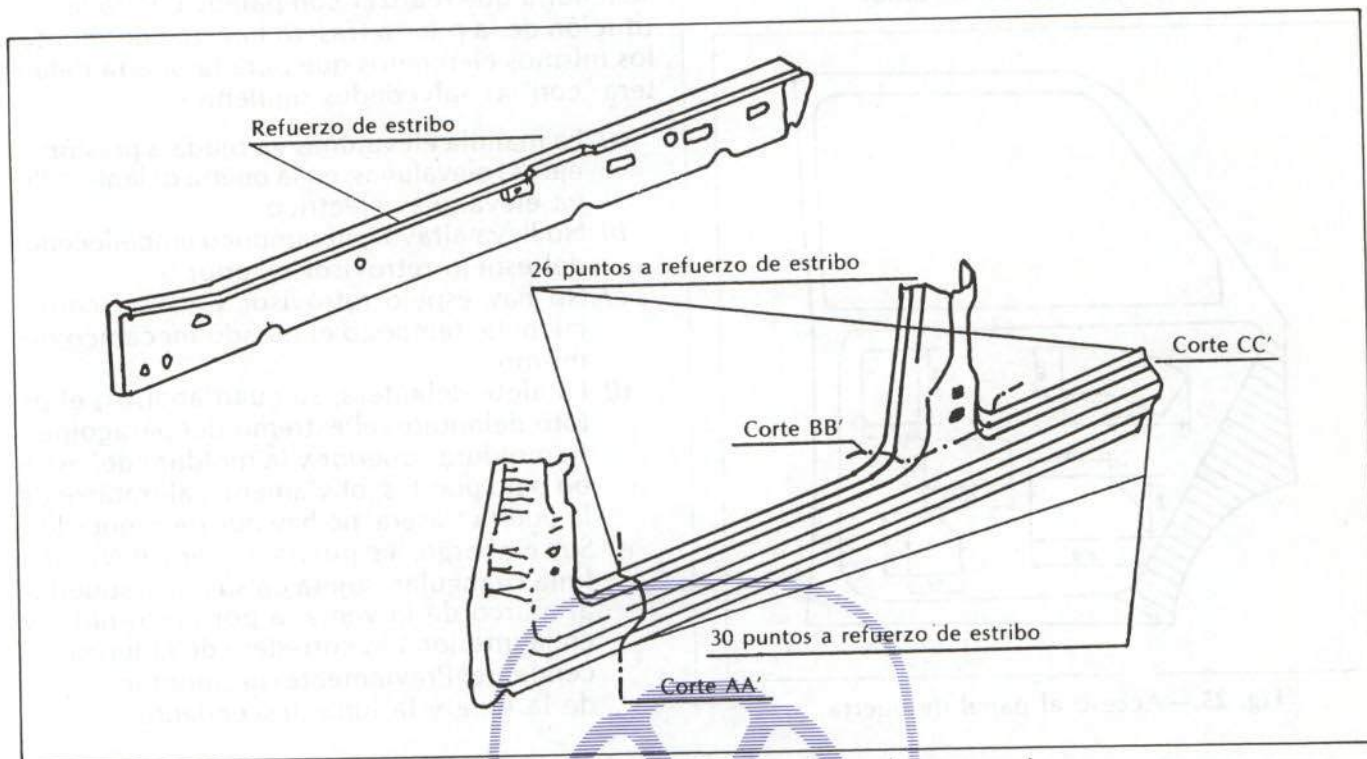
Unión del estribo bajo puertas a la carrocería.
